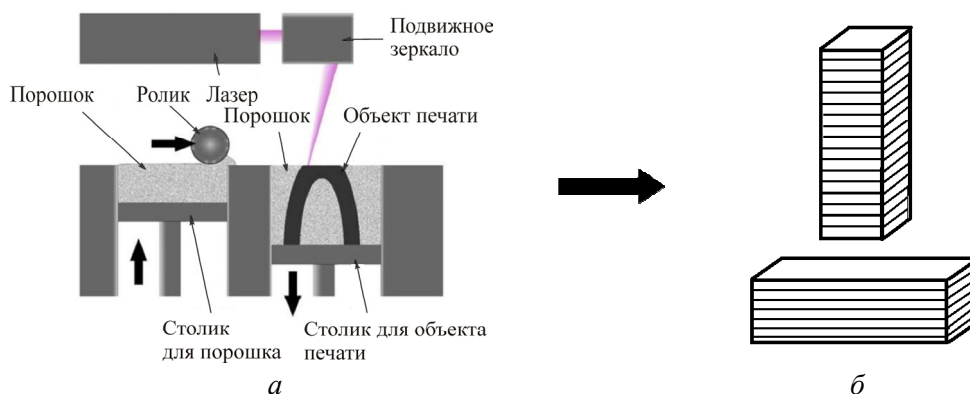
Принципиальная схема установки селективного лазерного сплавления (а) и схемы изготовления заготовок образцов для испытаний (б), выращенных в вертикальном и горизонтальном направлениях (горизонтальной штриховкой показано расположение сплавляемых слоев в заготовках)
